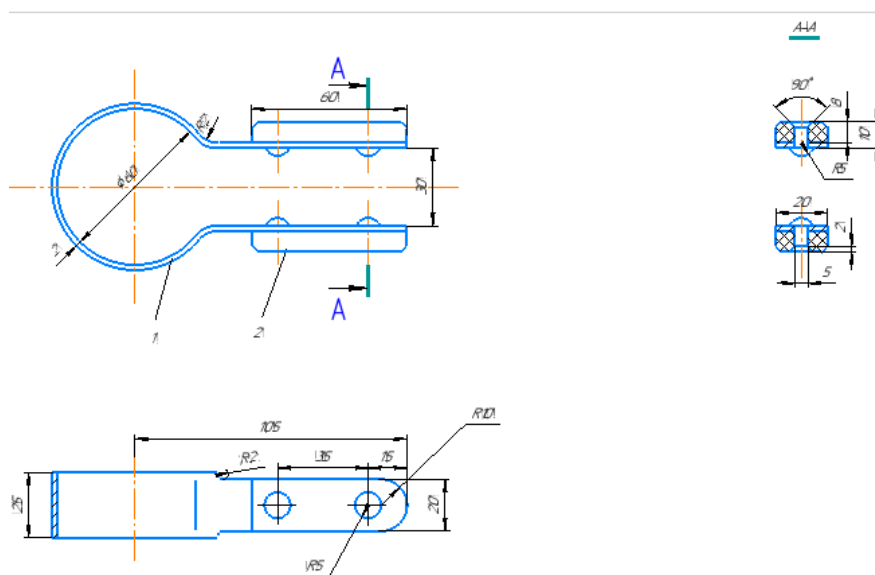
Приспособление для установки поршней в цилиндры компрессора
